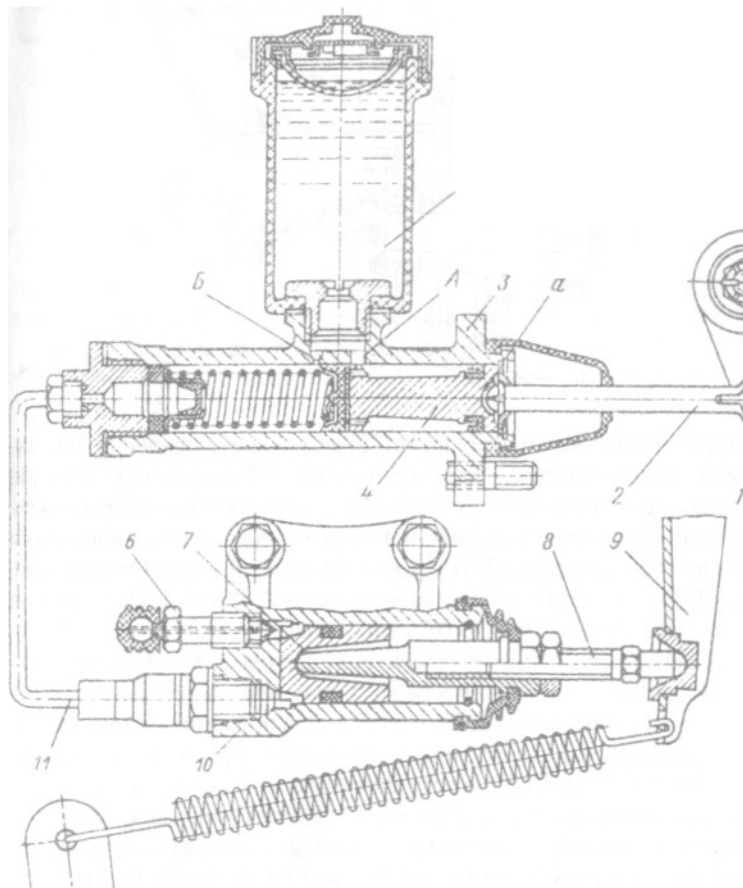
Гідралічний привод зчеплення легкового автомобіля: 1 - педаль; 2 - шток головного циліндра; 3 - головний циліндр; 4 - поршень; 5 - бачок; 6 клапан; 7 - поршень; 8 - шток робочого циліндра; 9 - вилка; 10 - робочий циліндр; 11 - трубопровід; А і Б - перепускний і компенсаційний отвори
